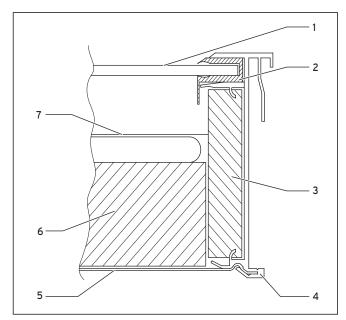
Coupe capteur plan Vaillant auroTHERM VFK 900
